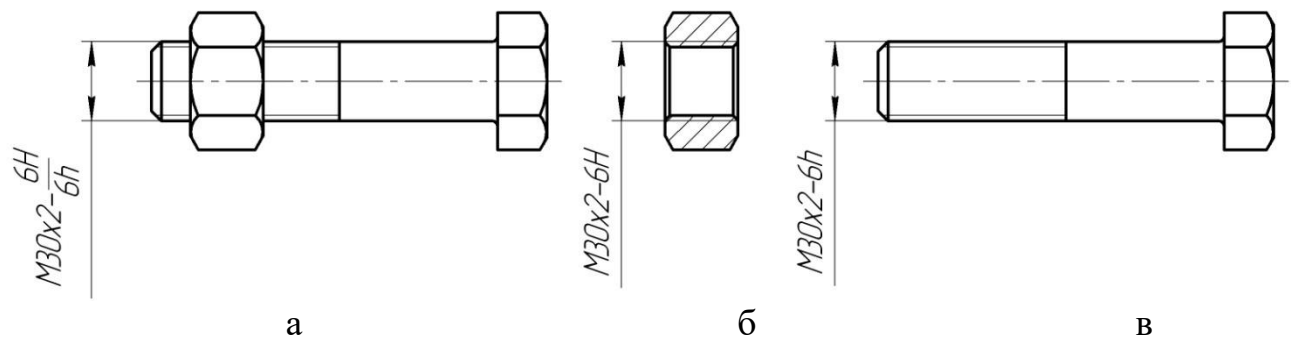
а – ескізи різьбового з'єднання; б – деталь з внутрішньою різзю; в – деталь з зовнішньою різзю.
